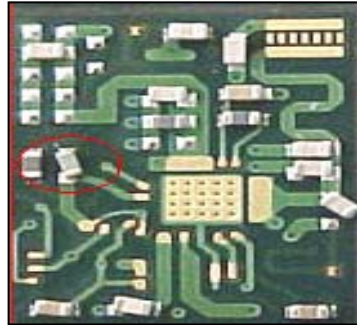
Alineación incorrecta de componente por desbalance en la tensión superficial de la soldadura.
